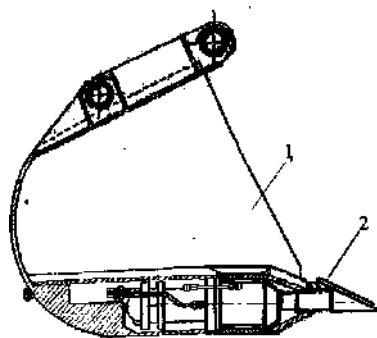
Конструкция ковша активного действия экскаватора экскаватора ЭО-4121 разработки СибАДИ: 1 - корпус ковша; 2 - ударные зубья
